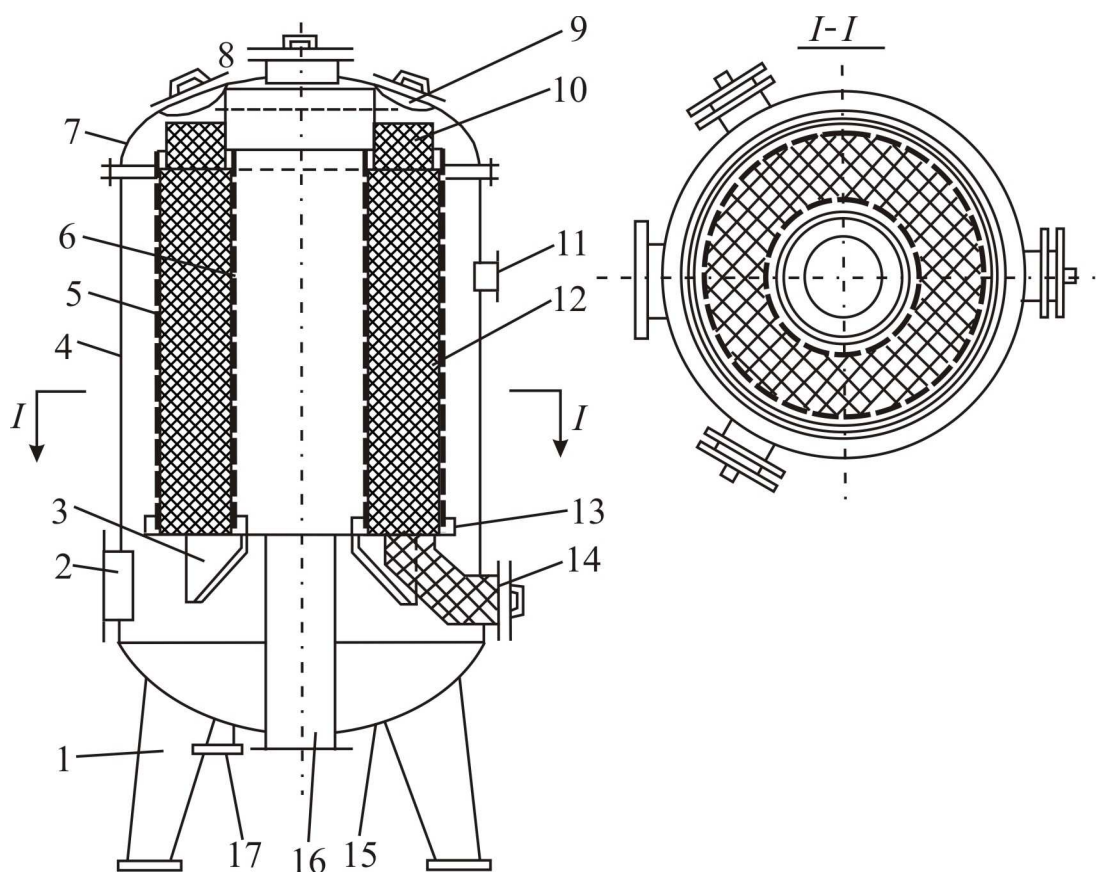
Кольцевой адсорбер ВТР: 1 - установочная лапа; 2 - штуцер для подачи паровоздушной смеси, сушильного и охлаждающего воздуха; 3 - опора для базы под цилиндры; 4 - корпус; 5, 6 - внешний и внутренний перфорированные цилиндры; 7 - крышка; 8 - смотровой люк; 9 - загрузочный люк; 10 - бункер-компенсатор; 11 - штуцер для предохранительного клапана; 12 - слой активного угля; 13 - база для цилиндров; 14 - разгрузочный люк; 15 - днище; 16 - штуцер для отвода очищенного и отработанного воздуха и для подачи водяного пара; 17 - штуцер для отвода паров и конденсата при десорбции и для подачи воды
